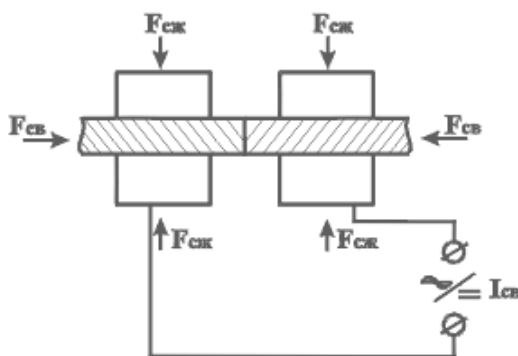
Схема стыковой контактной сварки.
